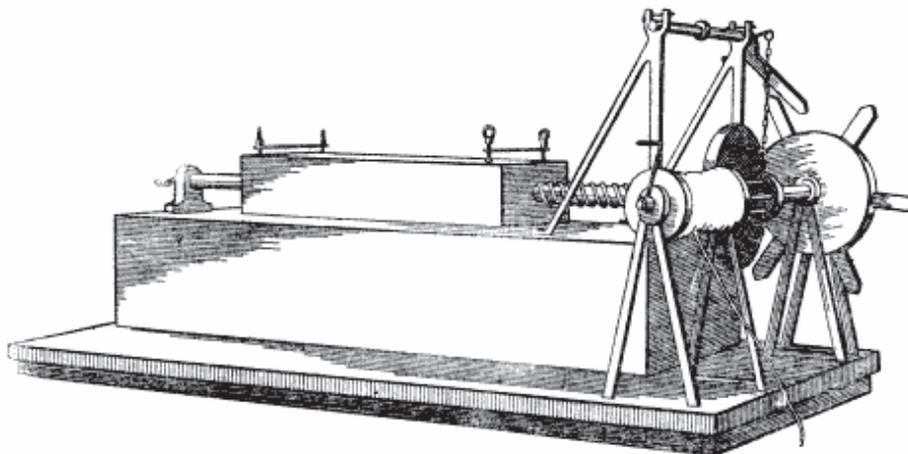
Станок для насечки напильников конструкции Леонардо да Винчи [2]
